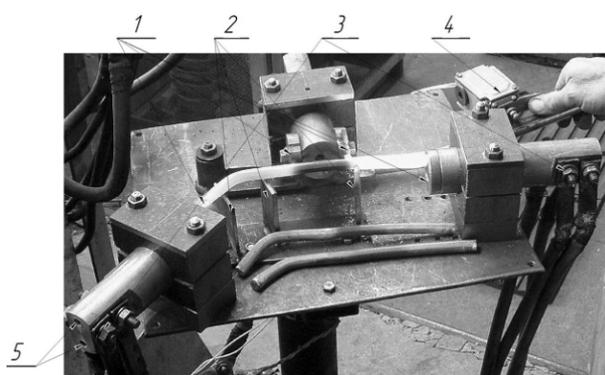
Устройство для нагрева заготовок браншей: 1 - электроды; 2 - упоры; 3 - крепление кабелей электропитания; 4 - рычаг прижима заготовки; 5 - подвод воды для охлаждения электродов
